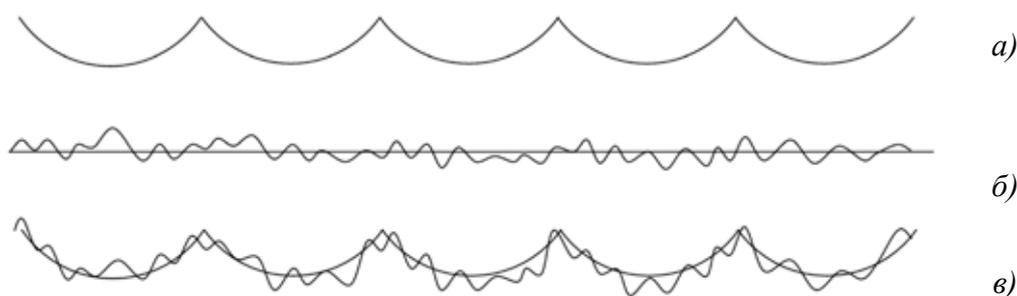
Схема образования профиля шероховатости поверхности при токарной обработке
